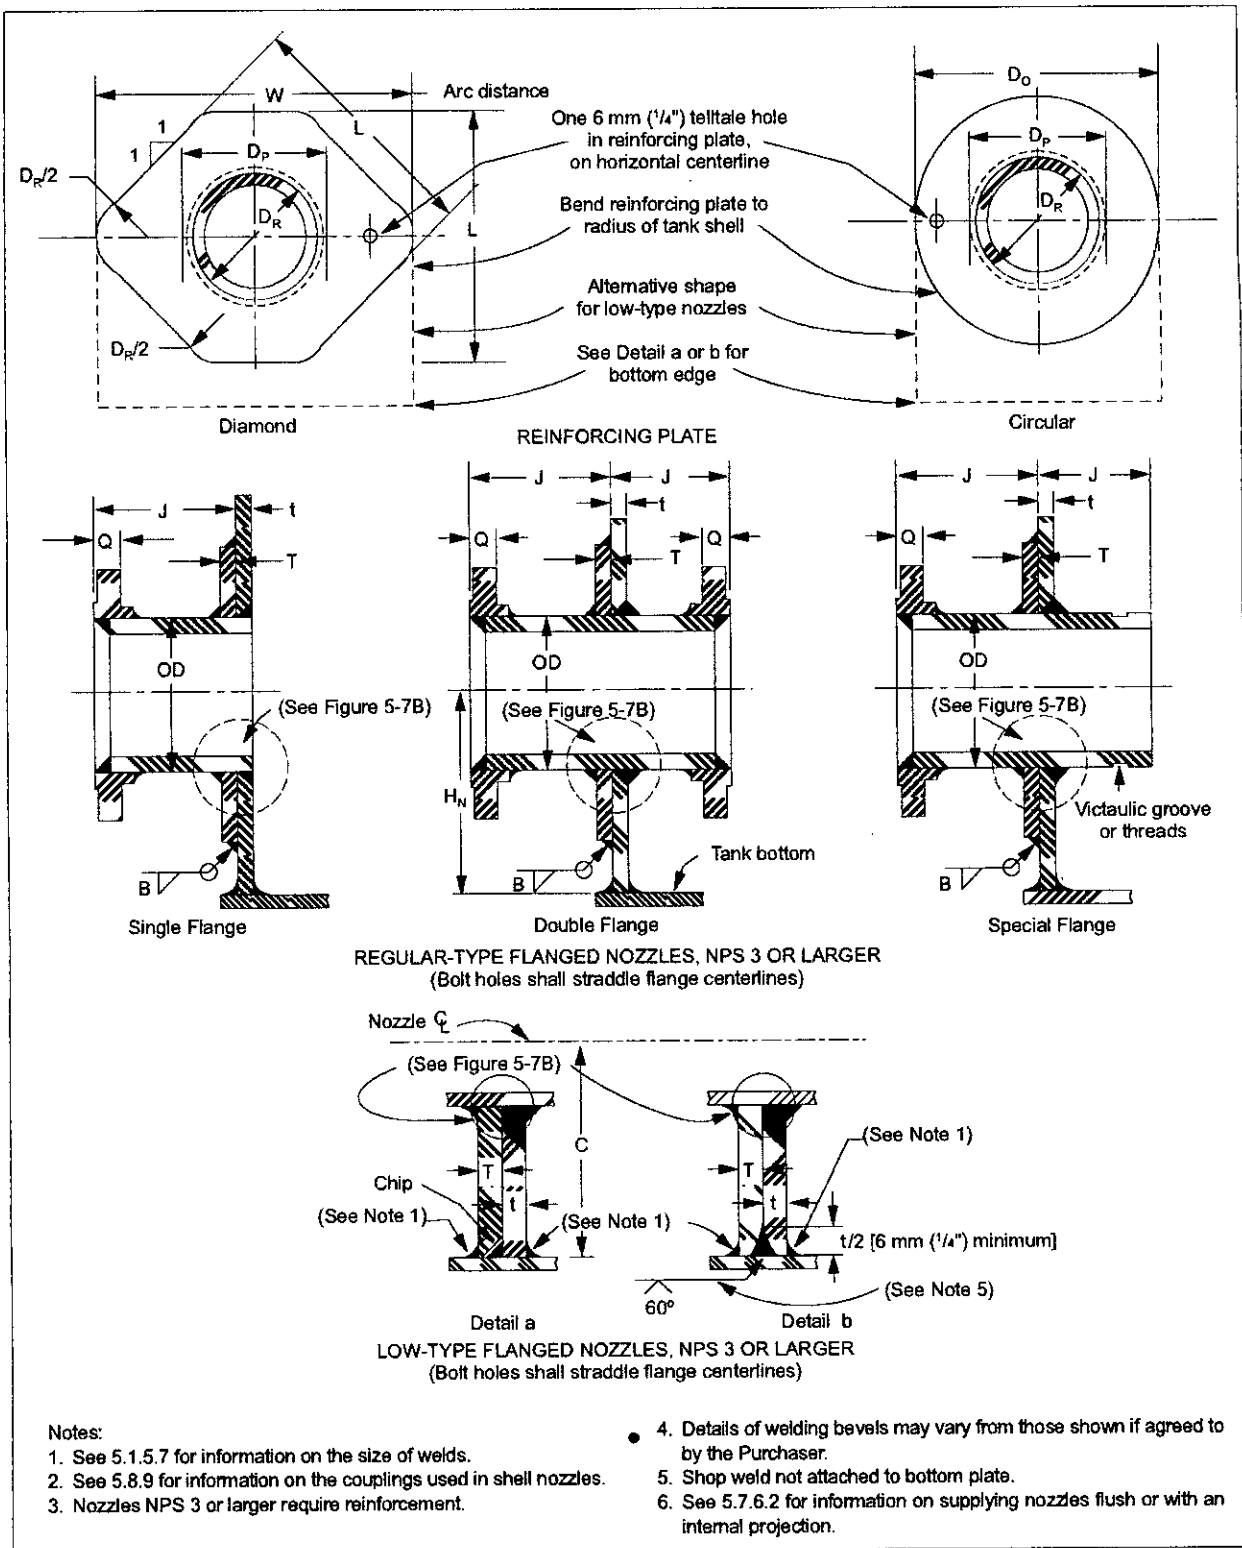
Detalle de conexiones y planchas de refuerzo.
